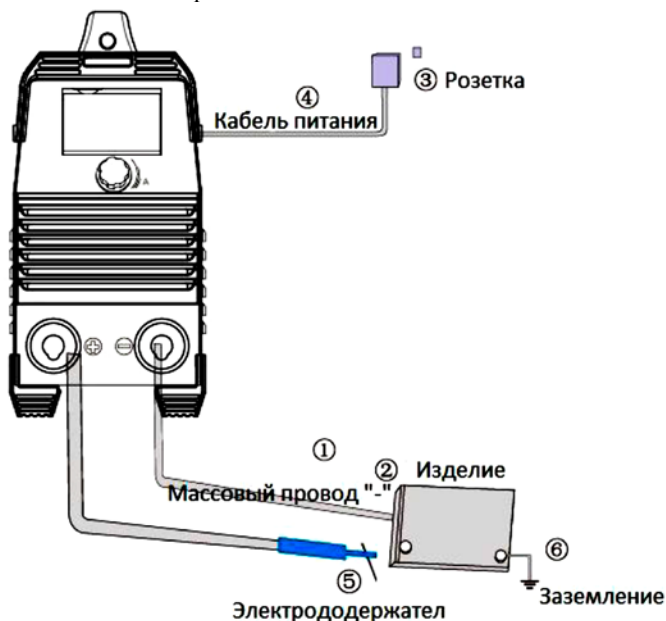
Схема подключения оборудования для ММА сварки
